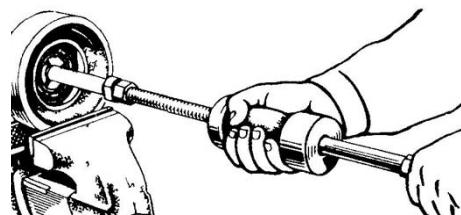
Выпрессовка подшипника № 209 из барабана включения.
